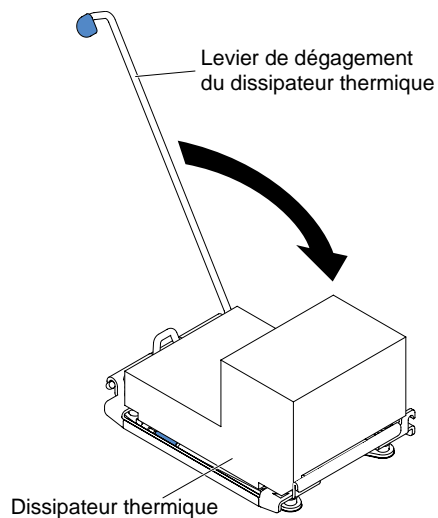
Levier de dégagement du module de fixation du dissipateur thermique
